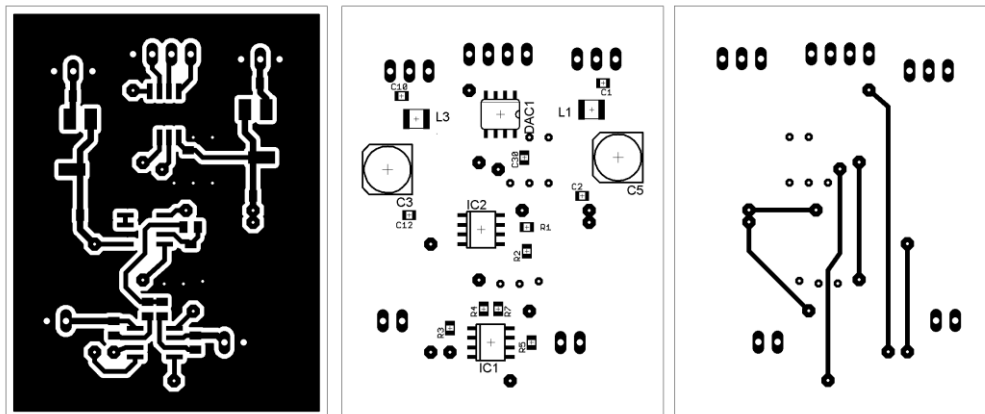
PCB a osadzovací plán rozšiřovača portov 44.1 x 31.8 mm
